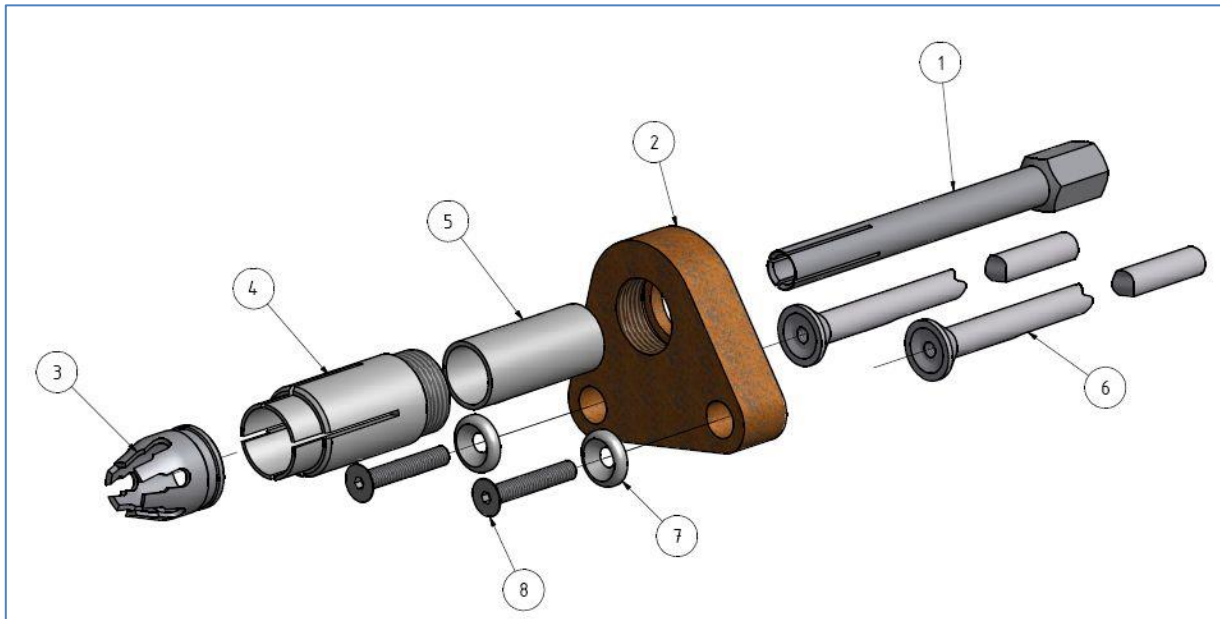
Stützeinrichtung für Gitterrostbefestigung
